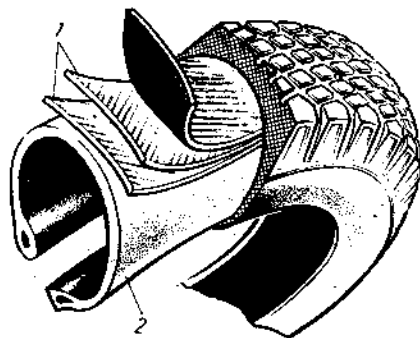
, Покришки шини типу Р: 1 _ шар брекера; 2 — каркас з радіально-розташованими нитками корду
